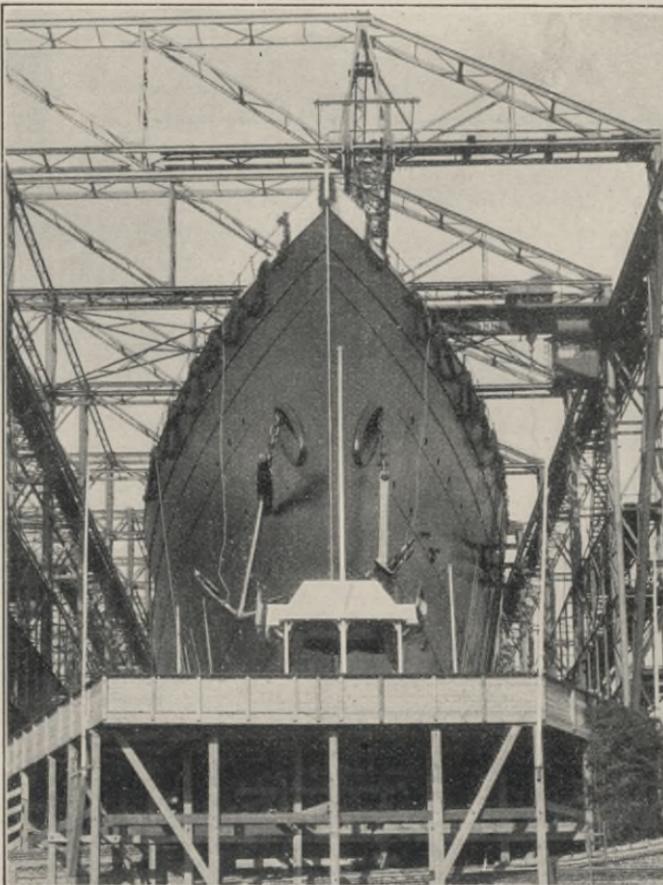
Der Dampfer „Kronprinzessin Cecilie“ fertig zum Stapellauf.
